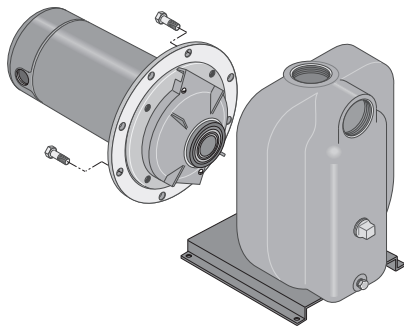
DESLICE EL MOTOR DE VUELTA A SU LUGAR
